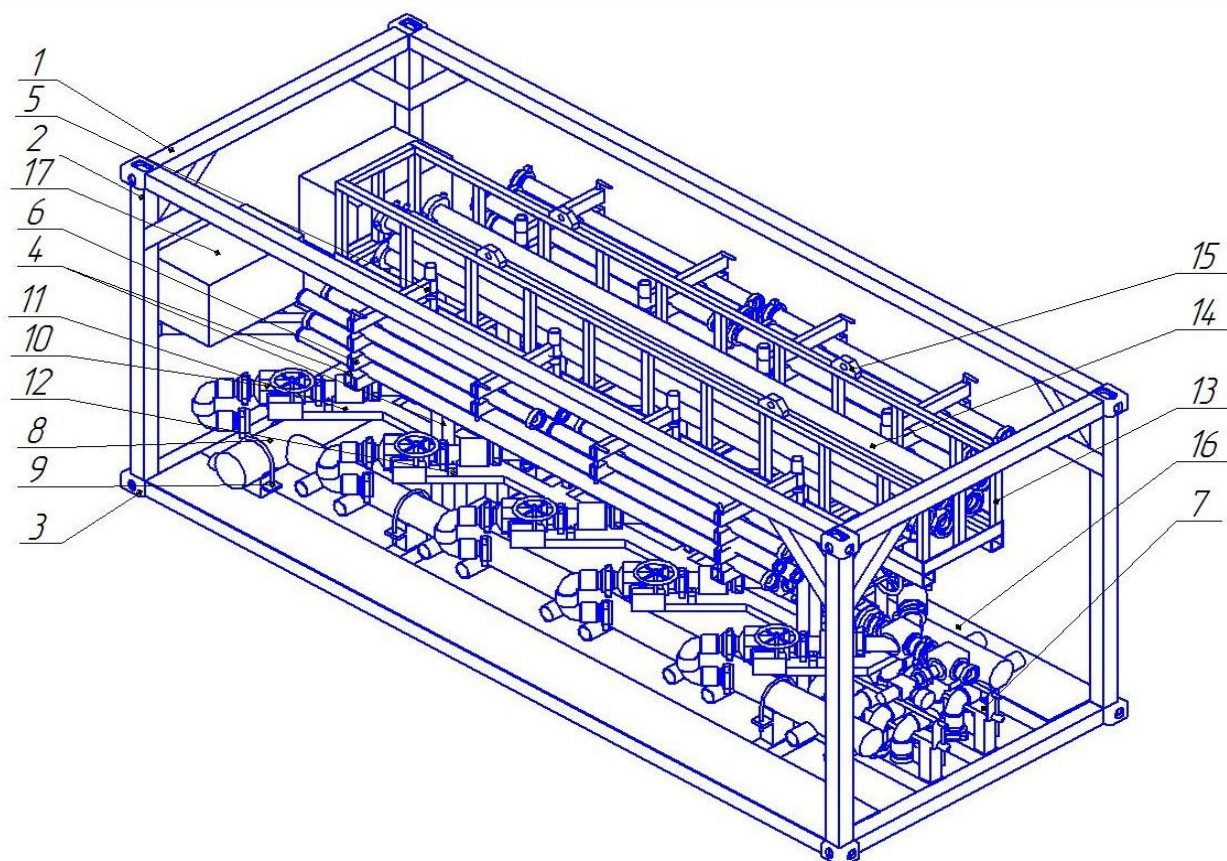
Эскизный чертеж блока манифольдов рамной конструкции контейнерного типа
